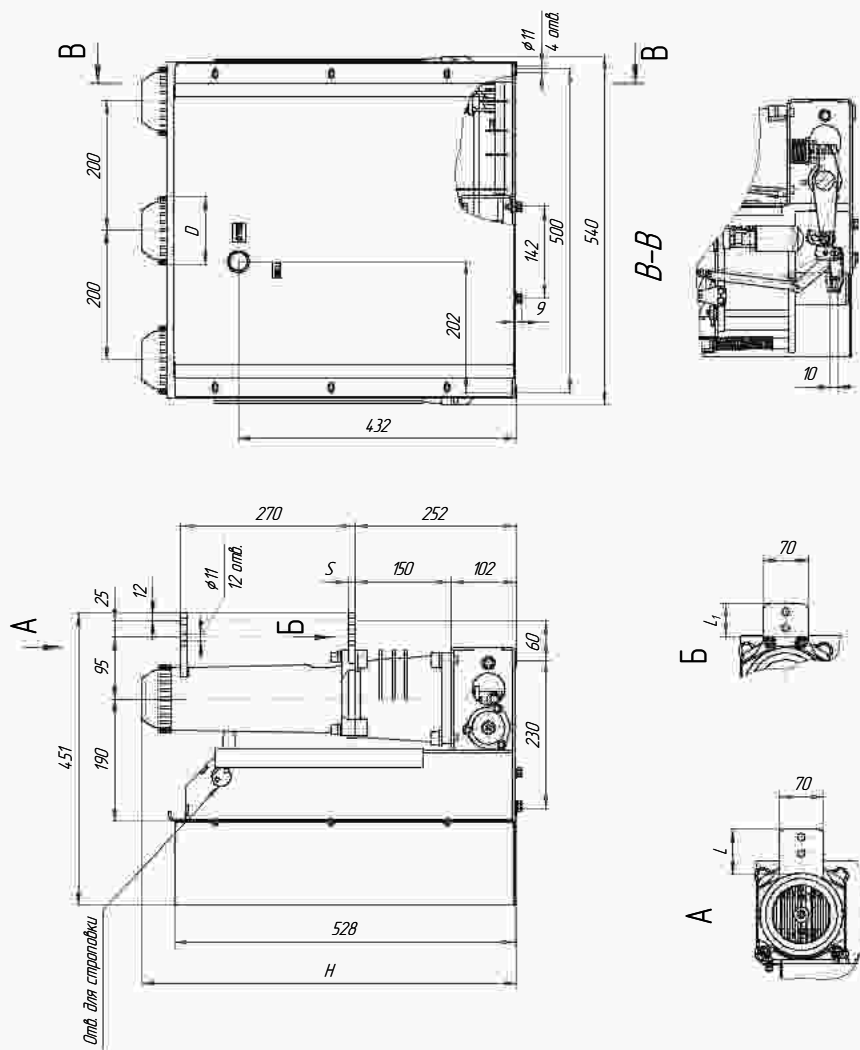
Габаритные, присоединительные и установочные размеры выключателя типа ВВУ-СЭЩ-З-10-20(31,5)/η (СЭЩ-70)
